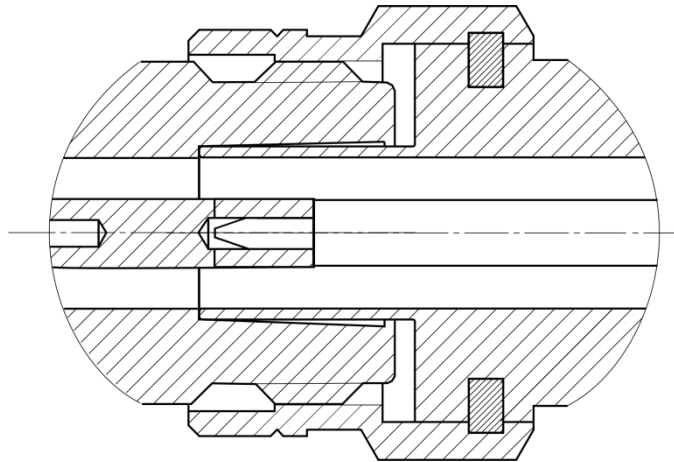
Соединители тип N и III (розетка слева, вилка справа)
